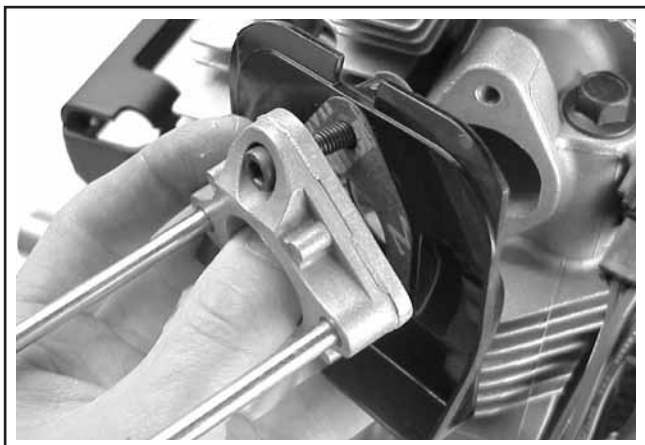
Retirer l'adaptateur du carburateur et le déflecteur thermique.
